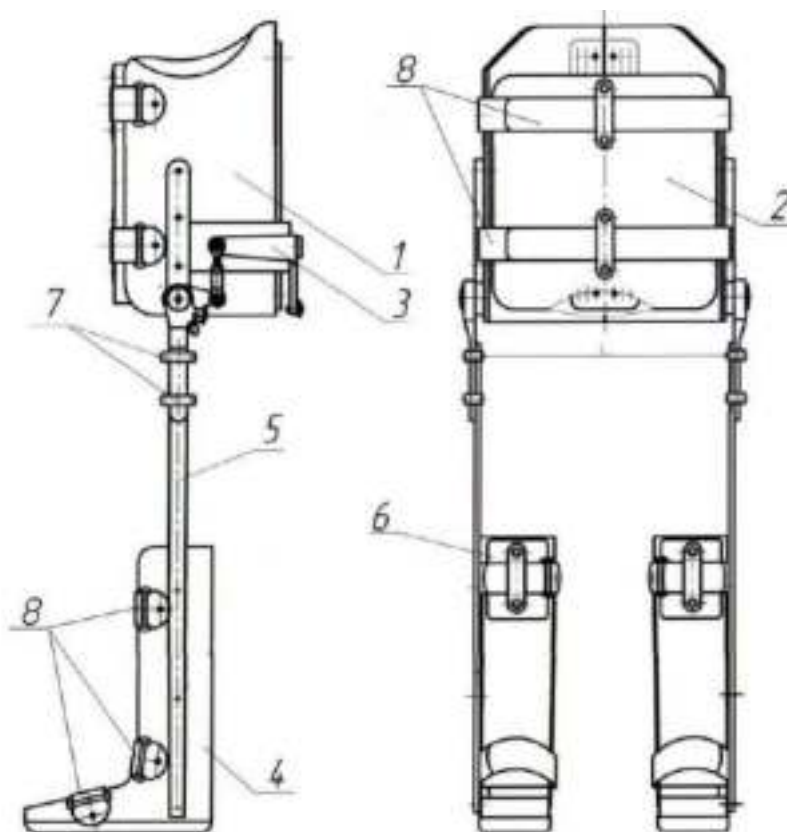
Загальний вигляд типорозмірного RGO
